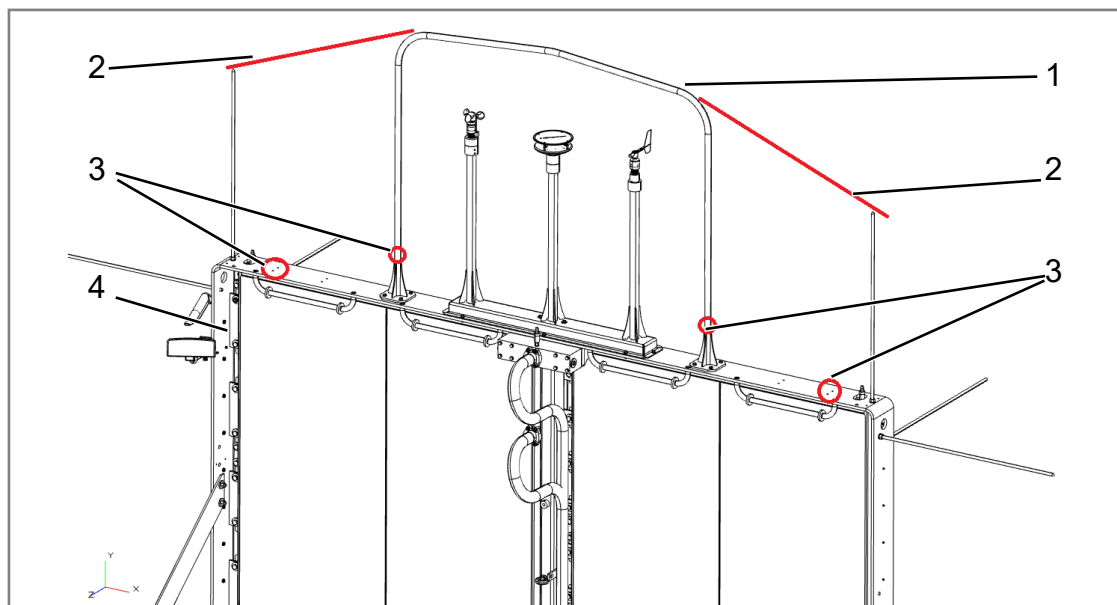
Ansicht des Passivkühlers Delta4000 von vorn (Rotor)
